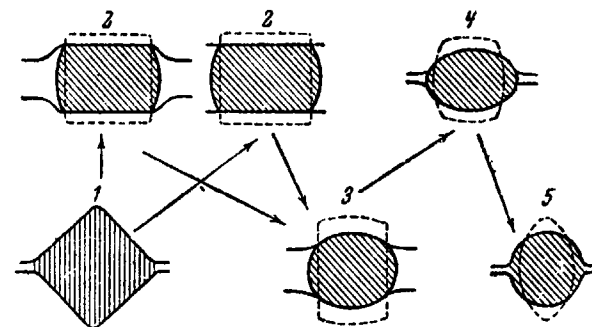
Схема калибровки круглой стали с применением ребрового калибра
